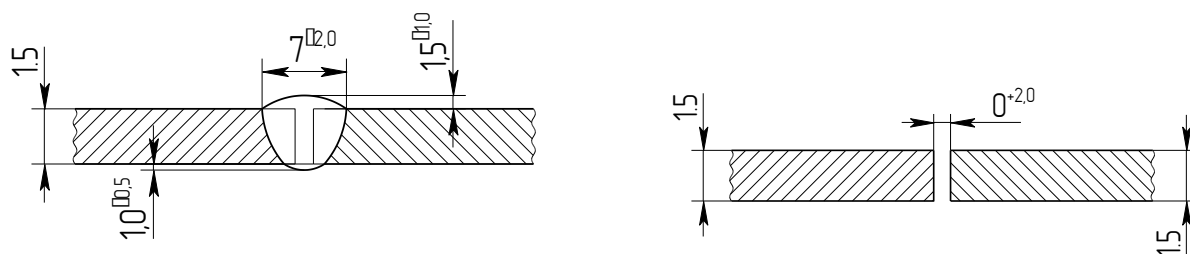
Конструктивные элементы сварного соединения С2
